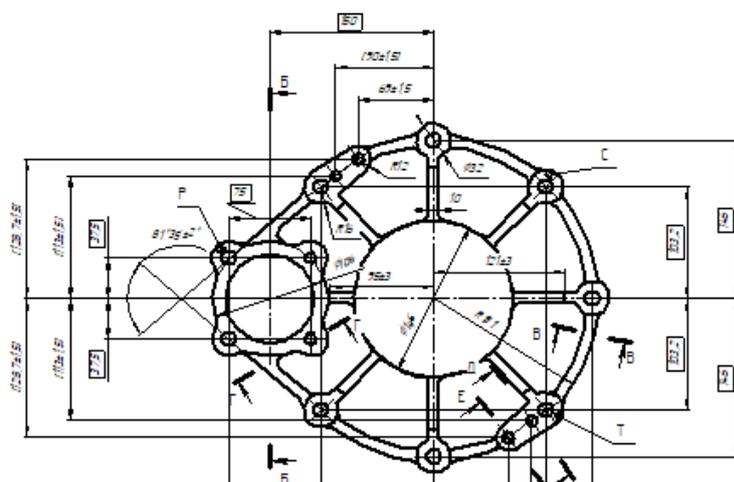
Чертеж детали – увеличенный фрагмент
